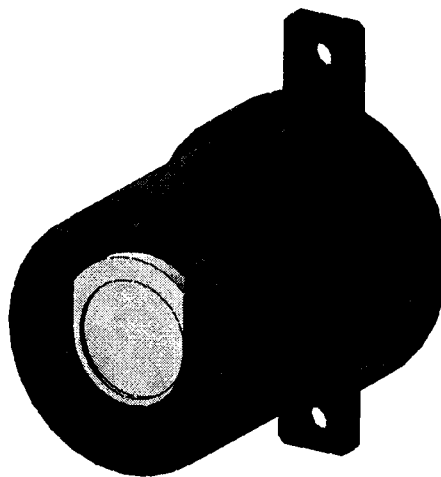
Общий вид штатного держателя с размещенным источником в «кармашке»
